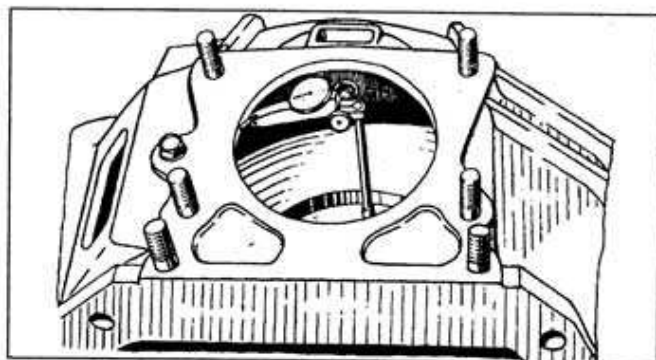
Проверка concentричности отверстия картера сцепления с осью коленчатого вала приспособлением 24-У-114625
